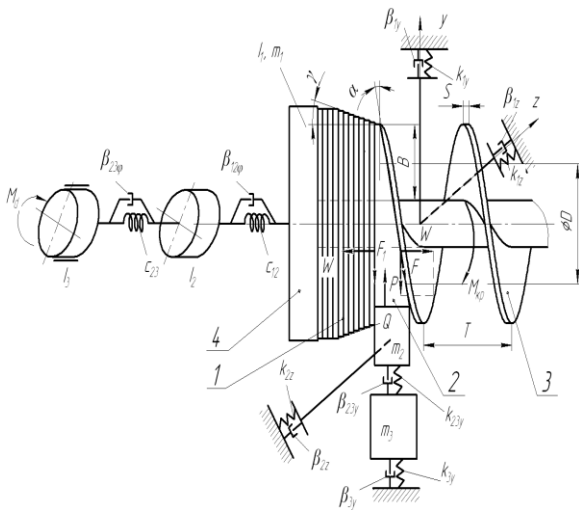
Розрахункова схема процесу калібрування витка конічної гвинтової заготовки на крок: 1 – щільно навита конічна заготовка, 2 – клин; 3 – калібровані на крок T витки гвинтової заготовки; 4 – оправка для калібрування
